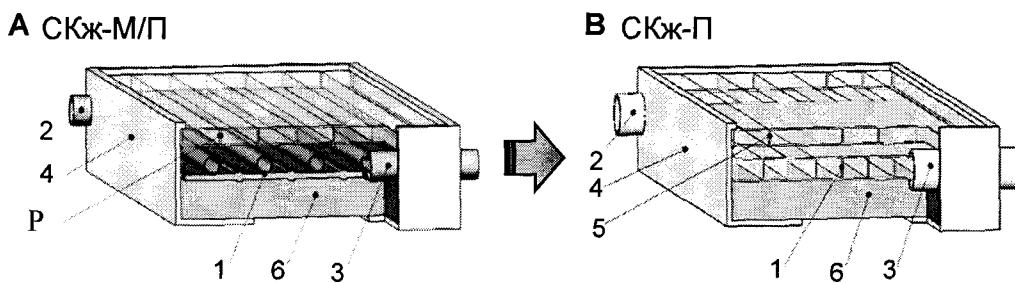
Метало-полимерный СКж (А) и полимерный СКж с воздушным зазором (В): Обозначения см. на рисунке 4
